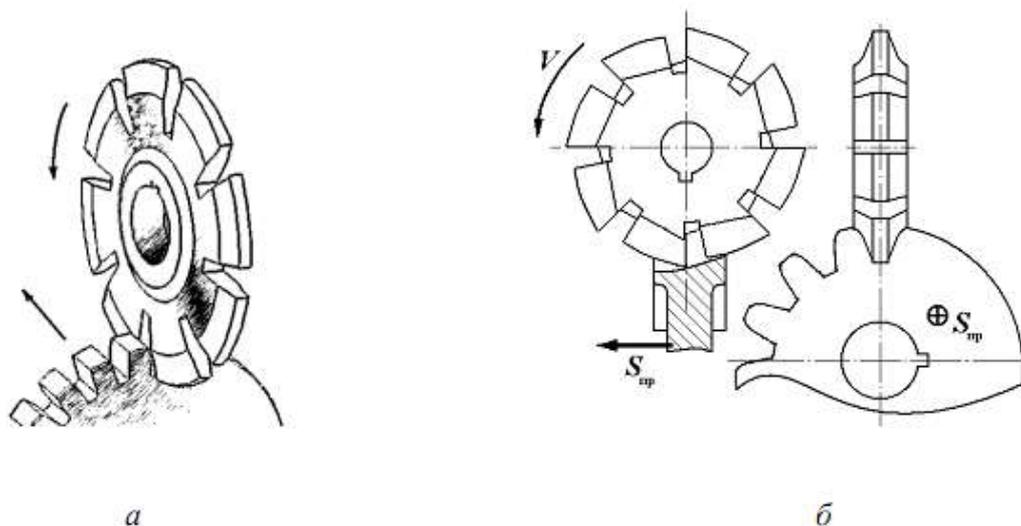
Обработка зубчатых колес дисковыми модульными фрезами
